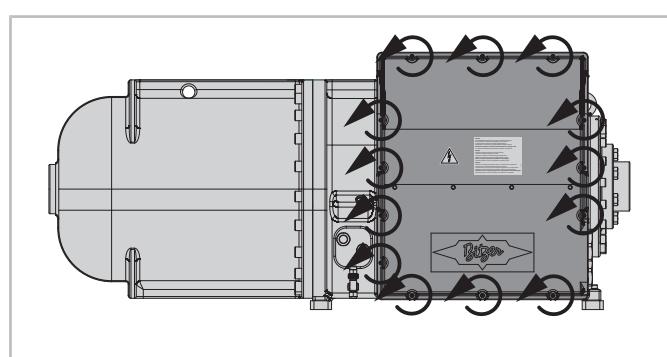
CSV.3: Снятие крышки корпуса FI.
